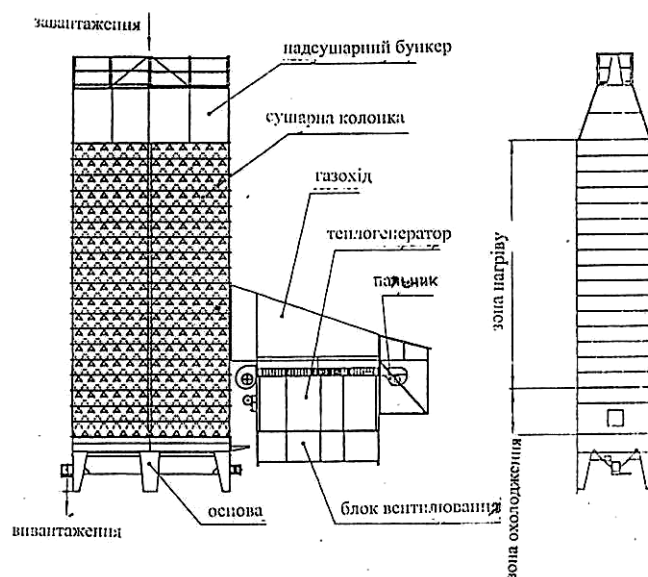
Принципова схема зерносушарки типу ЗШ
